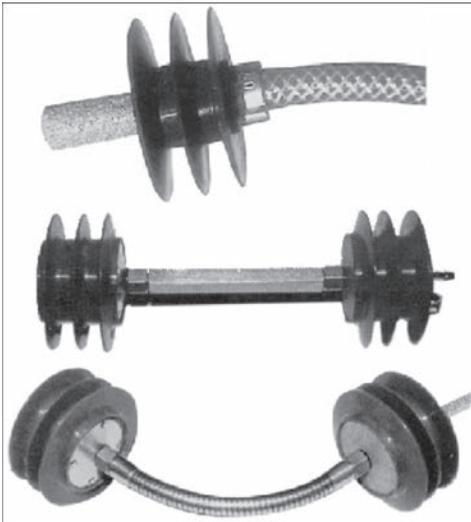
Вспомогательные приспособления для формирования обратной стороны шва
